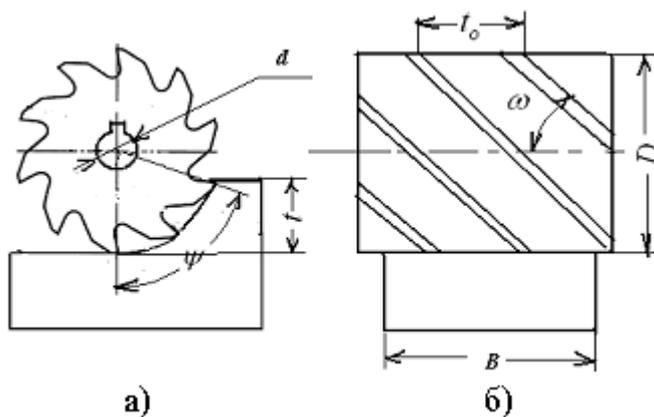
Схемы для определения числа зубьев цилиндрических фрез с прямыми (а) и винтовыми (б) зубьями:  $t$  – глубина резания;  $\Psi$  – угол контакта фрезы с обрабатываемой поверхностью заготовки;  $t_0$  – осевой шаг фрезы;  $\omega$  – угол наклона винтовых канавок, градус;  $B$  – ширина фрезерования;  $D$  – наружный диаметр фрезы;  $d$  – диаметр посадочного отверстия фрезы
